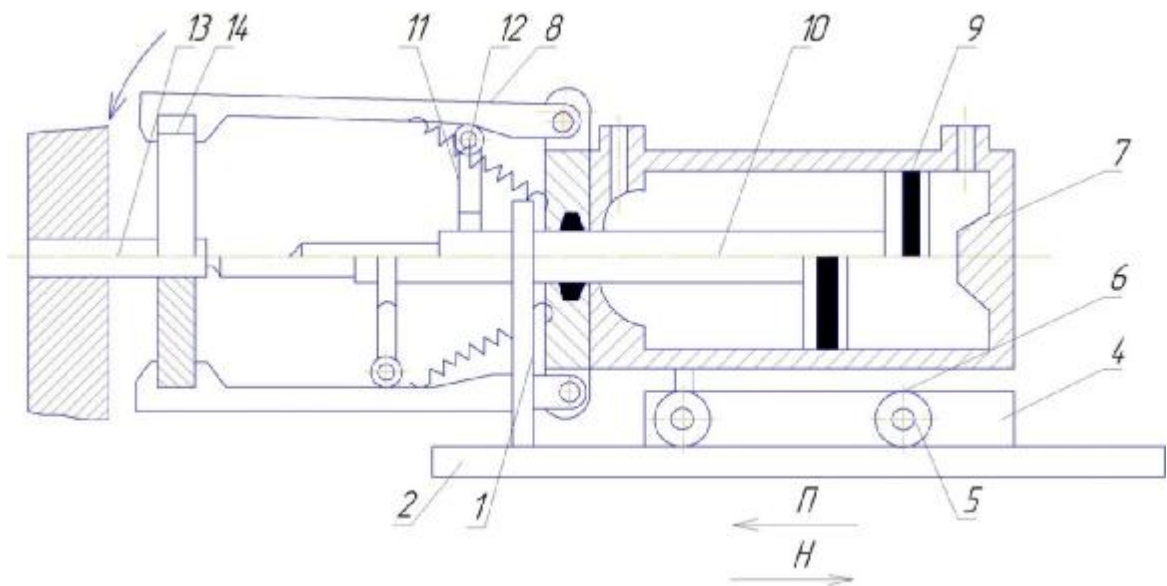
Стенд для демонтажу пресових з'єднань 1 – основа; 2 – обмежувач ходу; 3 – мікровимикач; 4 – напрямні; 7 – гідроциліндр; 8 – захоплювачі; 9 – поршень; 10 – силовий шток; 11 – траверса; 12 – переміщувальні ролики; 13 – вал; 14 – деталь, що знімається.
